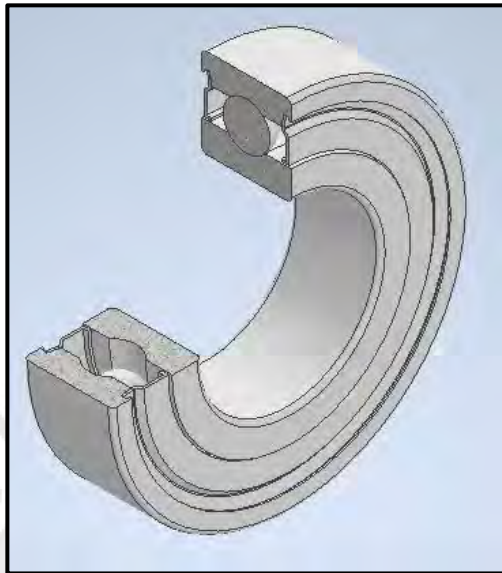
Vista 3/4 de rodamiento SKF 61901-2Z
